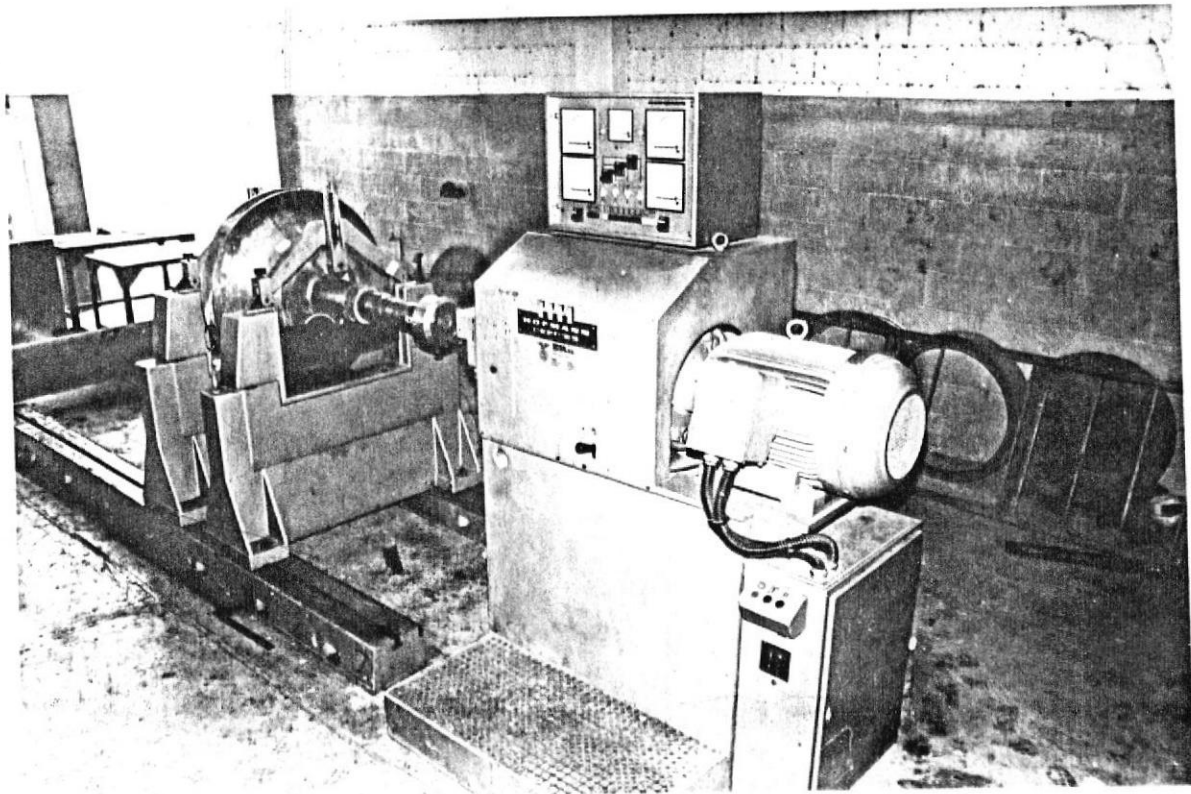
Impeler de la Motobomba # 5 en la Máquina Balanceadora Hoffman.
